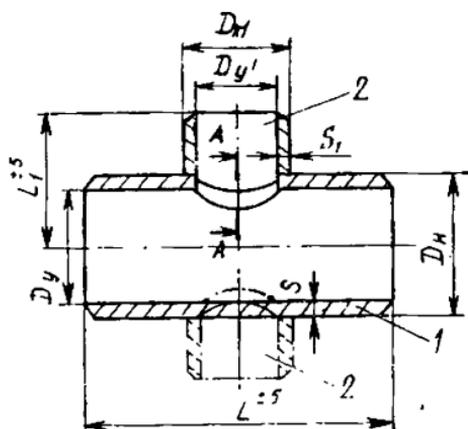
Тройник (крест) переходной сваркой
